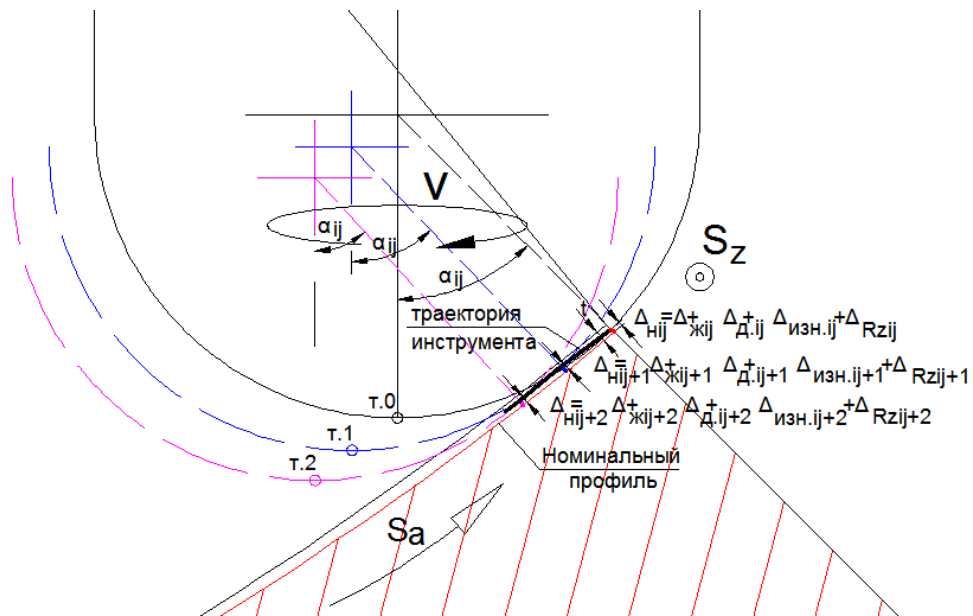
Схема геометрических отклонений обрабатываемой поверхности гравюры штампа поковки коленчатого вала
